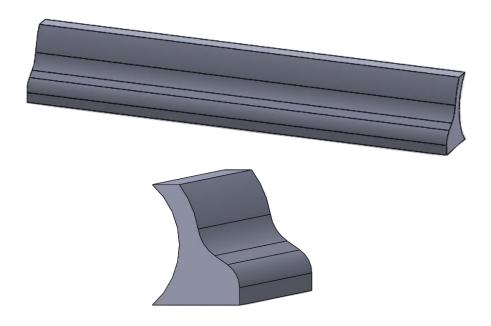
Detalle pieza unión Fuente: Elaboración Propia
